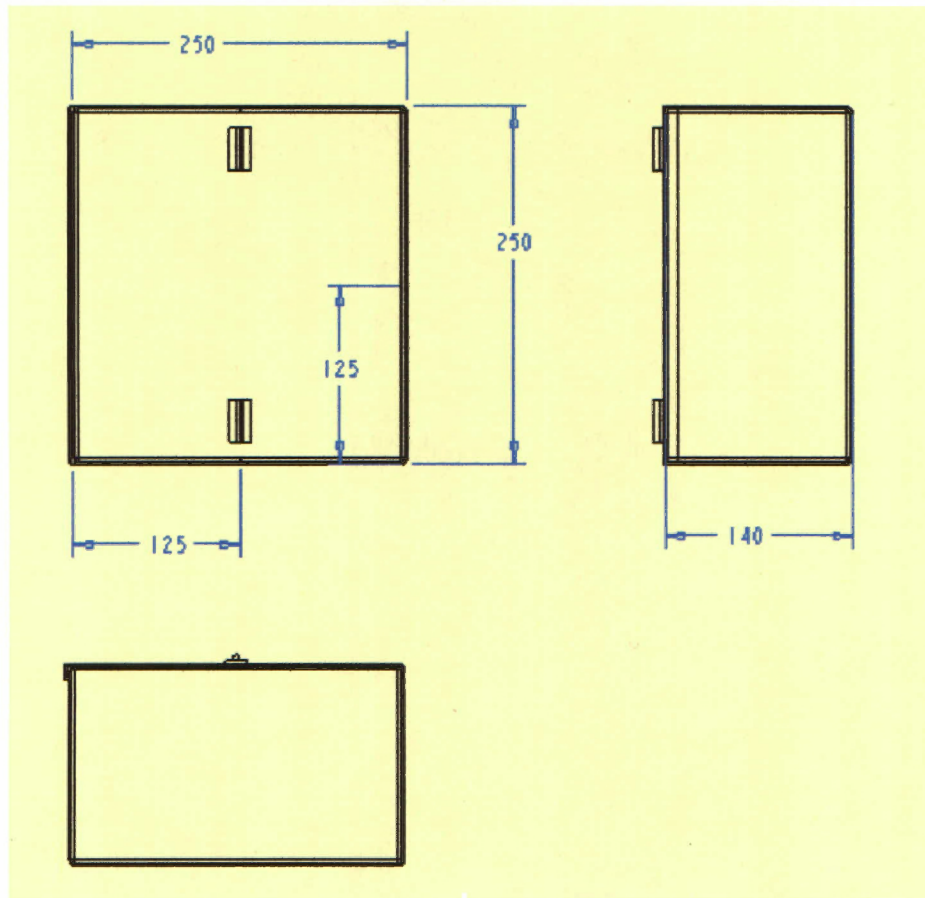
Dimensiones en cm de la base de aluminio. Diseño creado en ProE®
